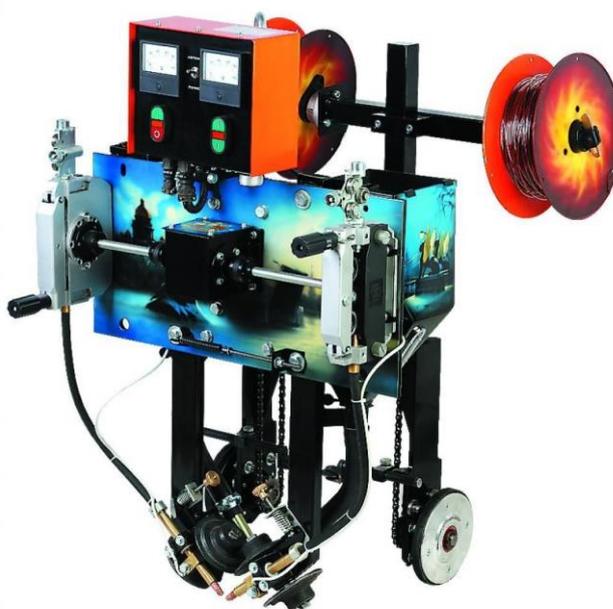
Сварочная установка по типу тракторной тележки марки 2ТС-16-04
